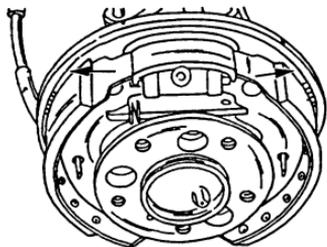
Демонтаж тормозных колодок и нажимной планки
